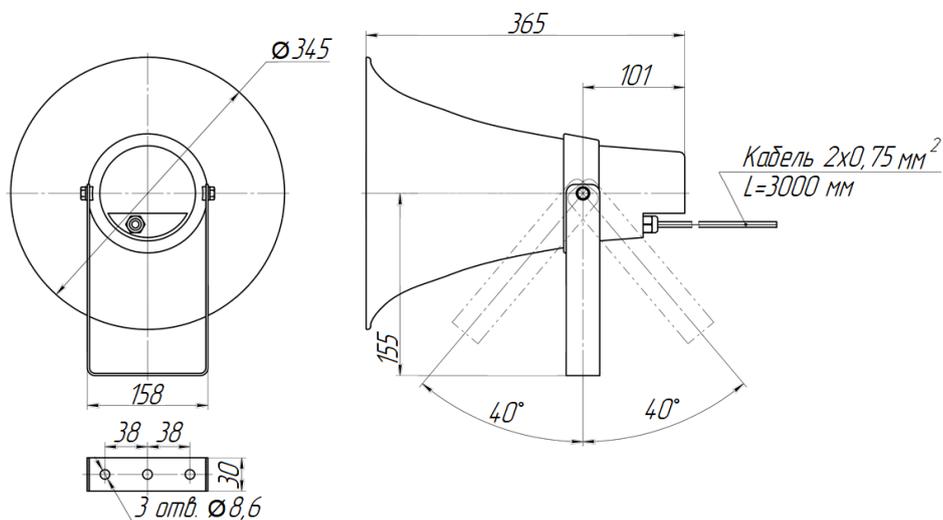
Габаритные и установочные размеры ГГ-8/100/50
